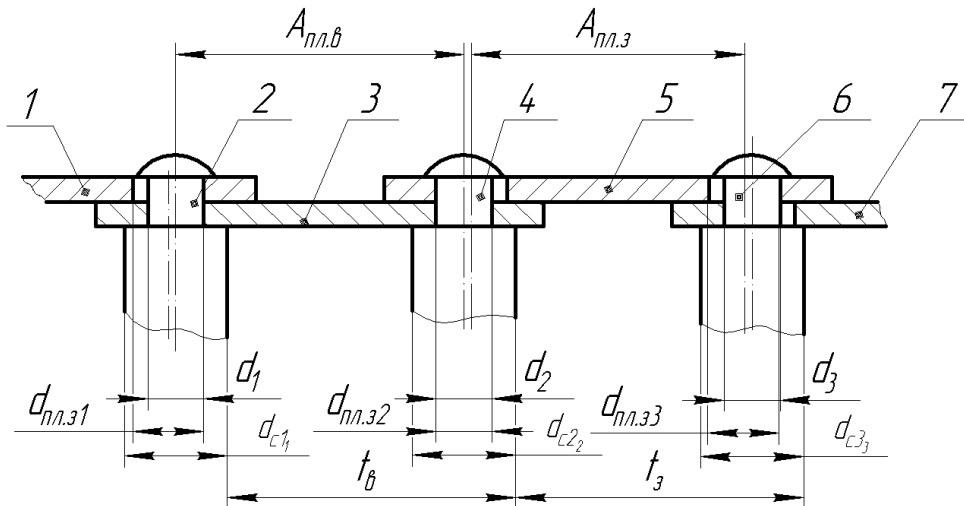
Розрахункова схема для визначення полів допусків на контактні кроки при з'єднанні співвісних валиків ПТБЛ з отворами внутрішніх пластин з натягом, а з отворами зовнішніх пластин із зазором: 1,5 – зовнішні пластини; 2,4,6, - валики ; 3,7 – внутрішні пластини
